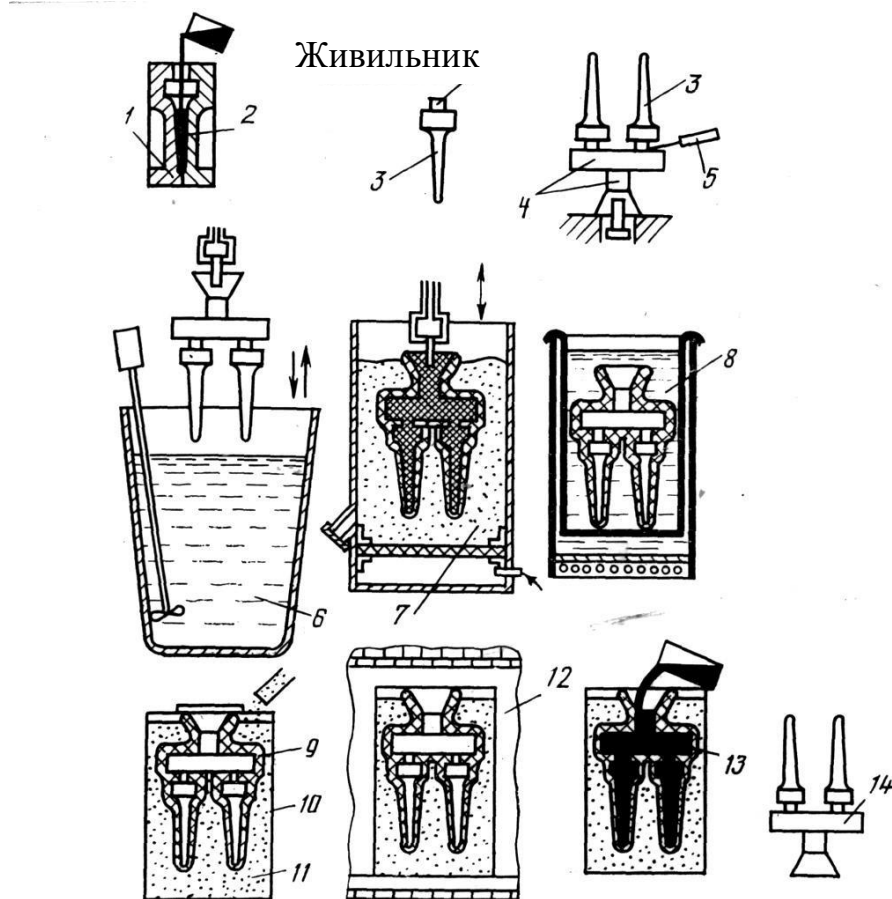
Схема виготовлення виливків за виплавлюваними моделями:
